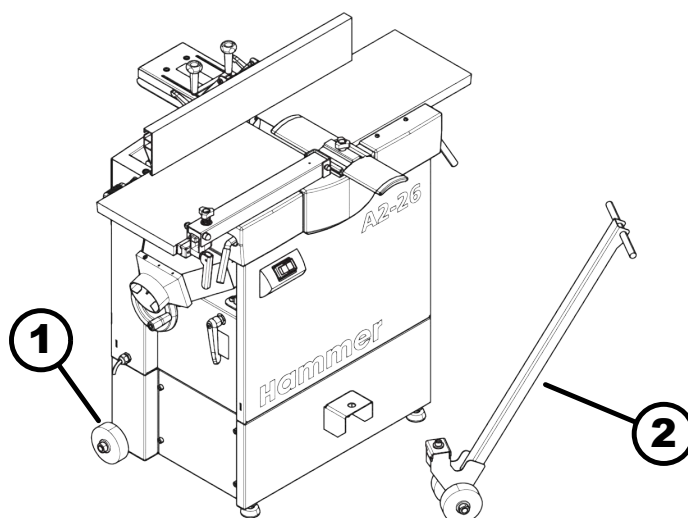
Transporte con dispositivo de desplazamiento y brazo elevador
